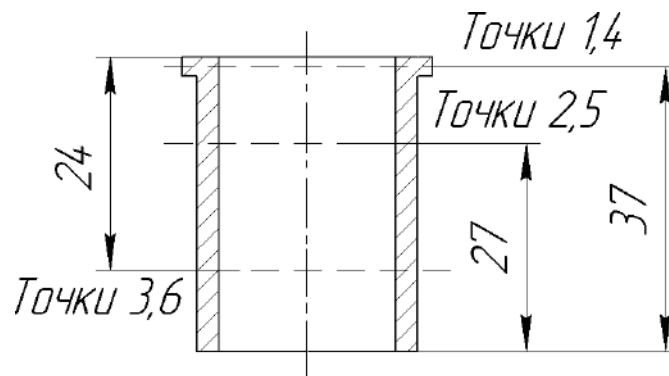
Схема розташування контрольних точок на робочій поверхні гільзи циліндра.
